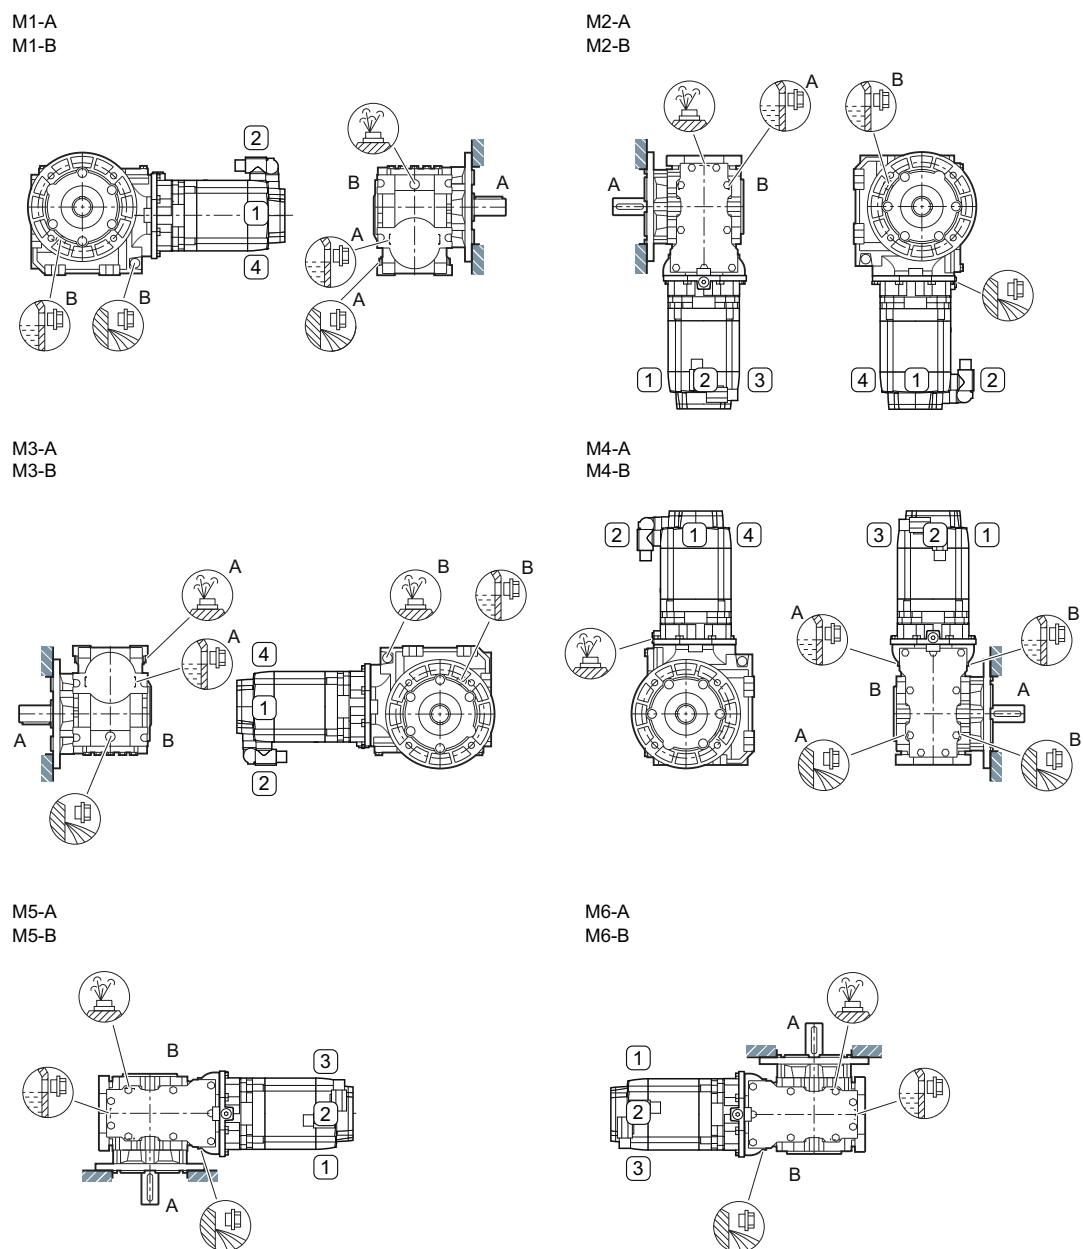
Einbaulagen für Servo-Stirnradsschneckengetriebemotor CF (Flanschausführung) und CAZ (Gehäuseflanschausführung), Baugröße 39A, 2-stufig
